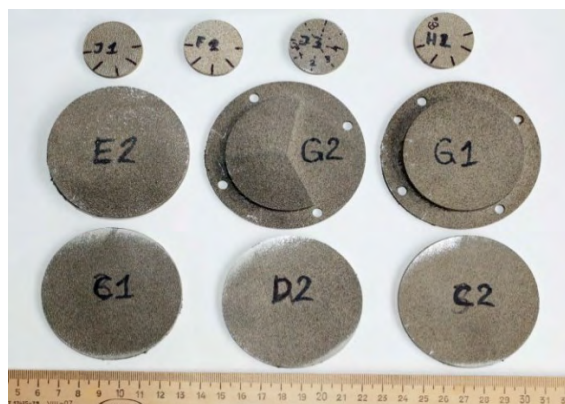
Образцы из стали изготовленные на 3D принтере
